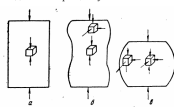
Схеми напружень при осіданні циліндричних заготовок:
